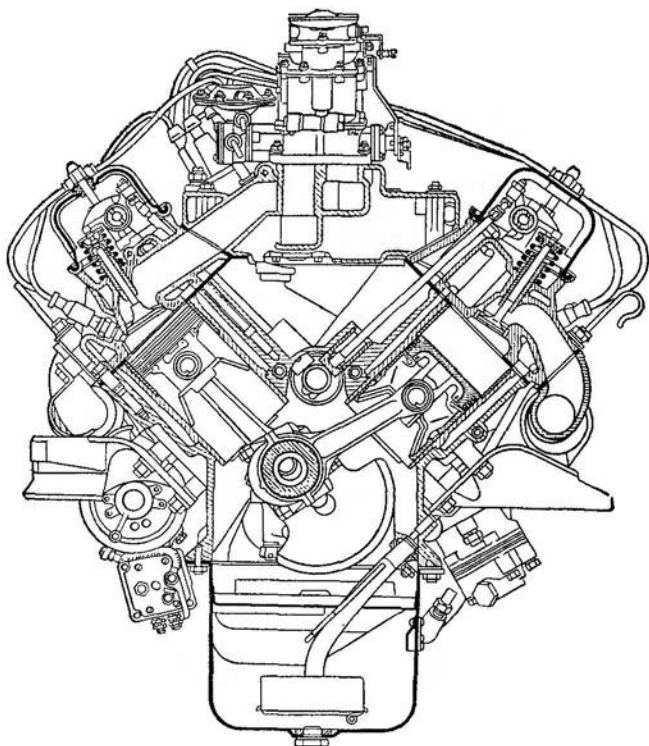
Поперечный разрез двигателя автомобиля ГАЗ-66
